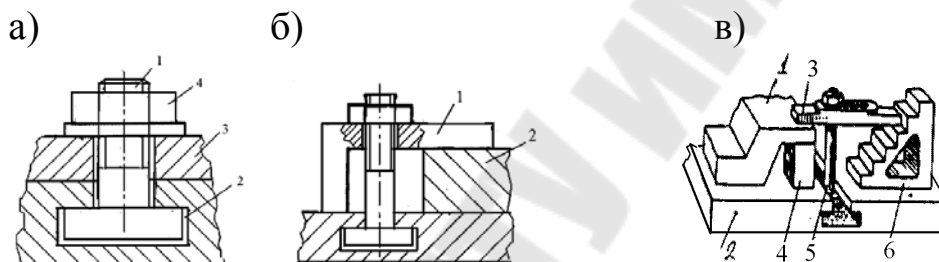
Схемы закрепления заготовок на столе сверлильного станка
